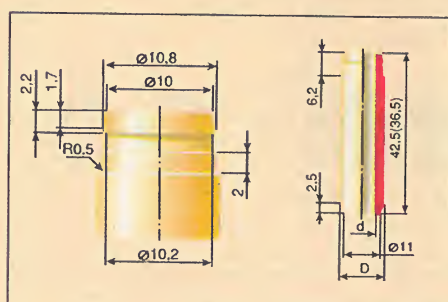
Направляющие втулки клапанов двигателя автомобиля "Ауди-100" (латунь). Короткая — для впускного клапана.
